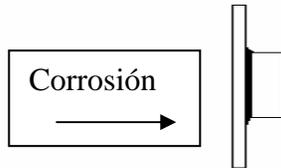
Muestra el desarrollo prematuro de corrosión provocada por quemaduras en la cara opuesta a la soldadura.
